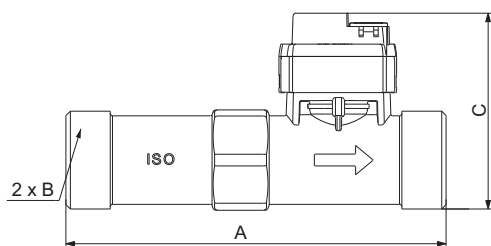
Размеры, VFS QT, 5-100 л/мин, с резьбовыми соединениями
